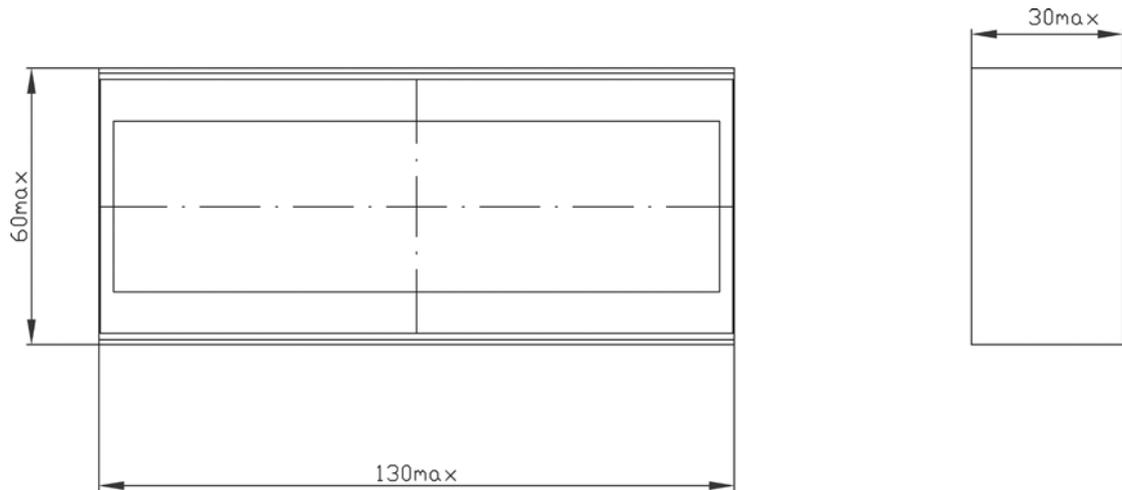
Габаритные размеры показывающего устройства ПУ-25
